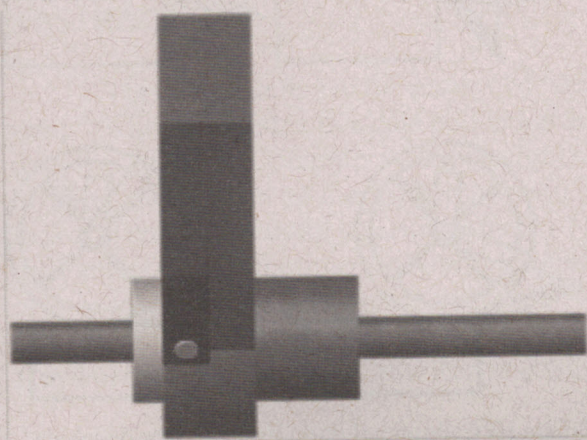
Eixo alongado juntamente com o apoio, rolamento e trava da rampa.
